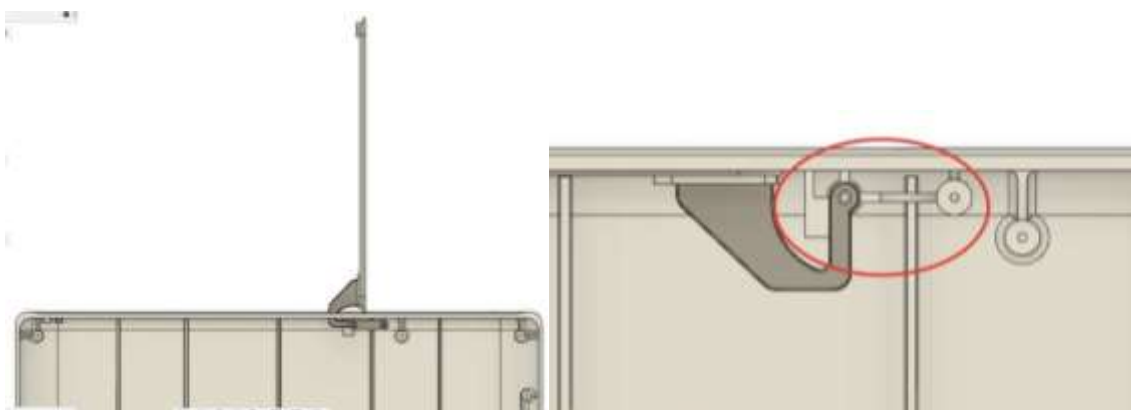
3Д модель крепления для дверцы поворотного и вариант его закрепления к корпусу
